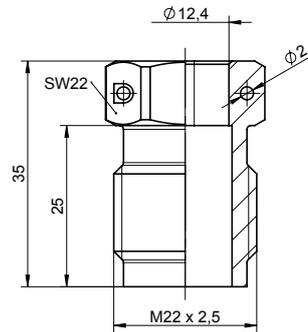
Montageadapter M22x2,5, Typ 6419A23A
